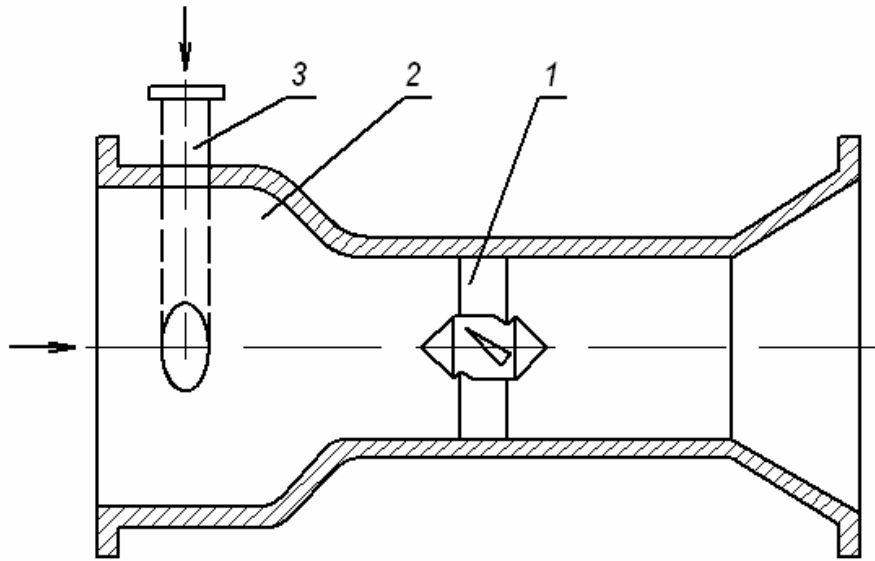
Кавітаційний змішувач з СК-крильчаткою: 1 – кавітатор-крильчатка; 2 – конфузор; 3 – патрубок
